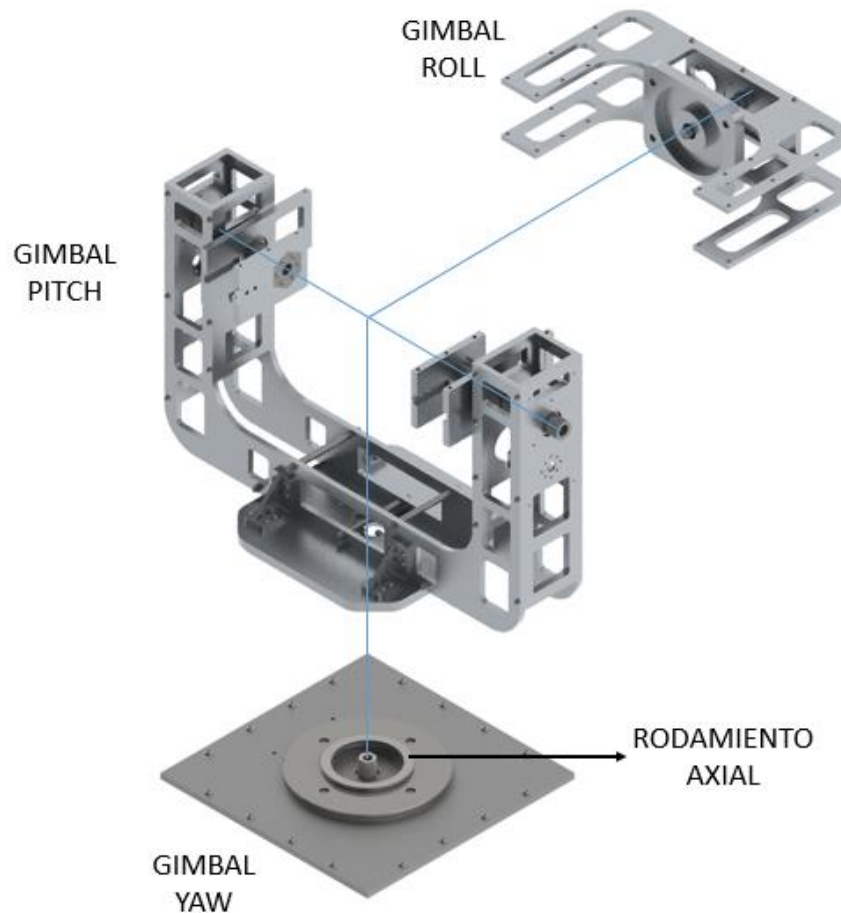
Placa de soporte del motor y el eje de estructura Gimbal Yaw.
